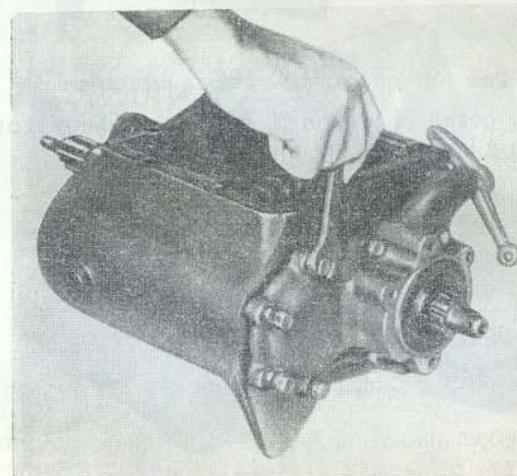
Установка крышки задних подшипников коробки передач автомобиля УАЗ-451М
